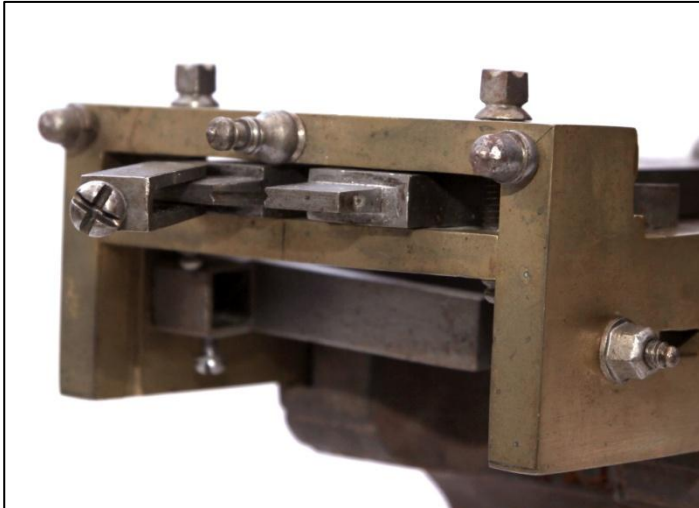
Spindeldok nr. 3952 med åben spindelbrille
